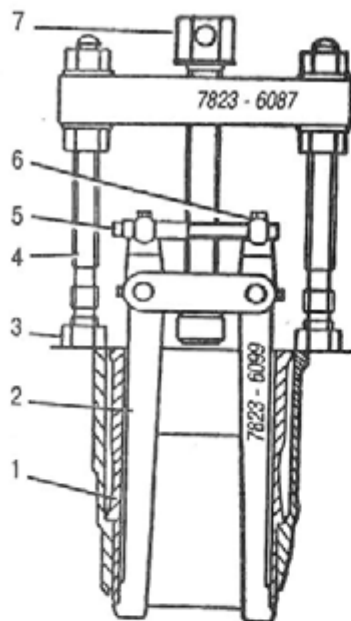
Выпрессовка гильзы из блока цилиндров комбинированным съемником:
